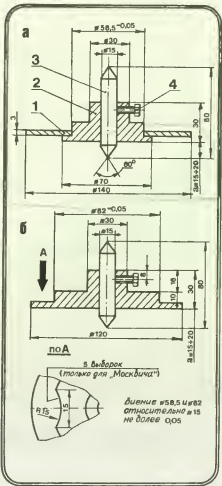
Схема балансировки иолеса: 1 — иолесо; 2 — приспособление; 3 — опора; 4 — центр тяжести иолеса.
